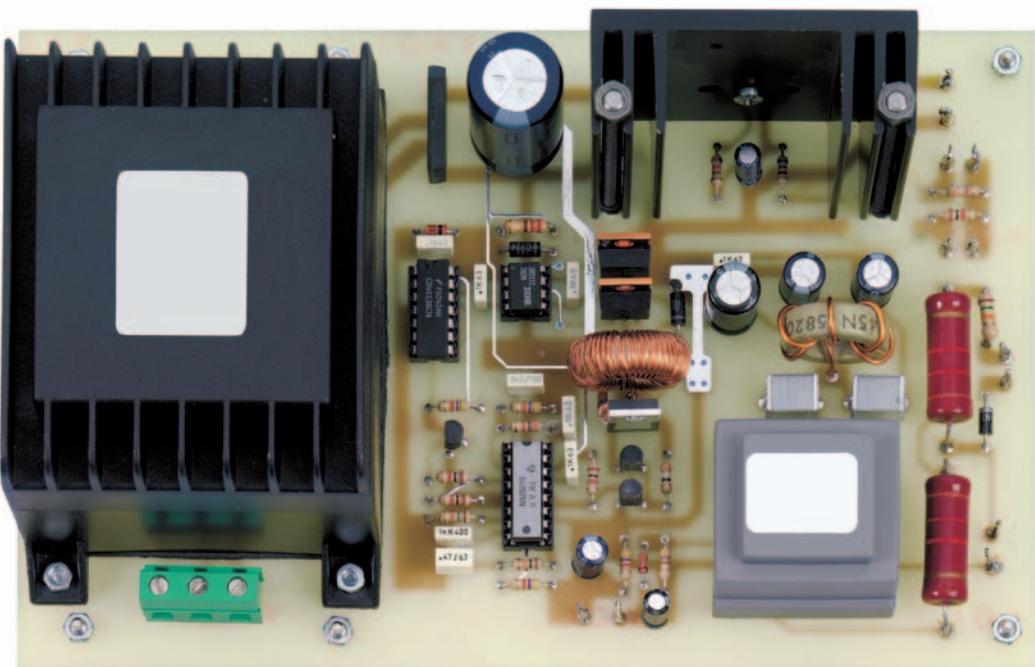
Photo d'un des prototypes de la platine du régénérateur de tube cathodique EN1659. Le dissipateur du régulateur IC3 a été montée (il est fixé au ci par deux boulons). Prêtez beaucoup d'attention au sens d'insertion des circuits intégrés qui ont un support et ne les installez qu'après montage de la platine dans son boîtier (voir figures 10 et 11).
